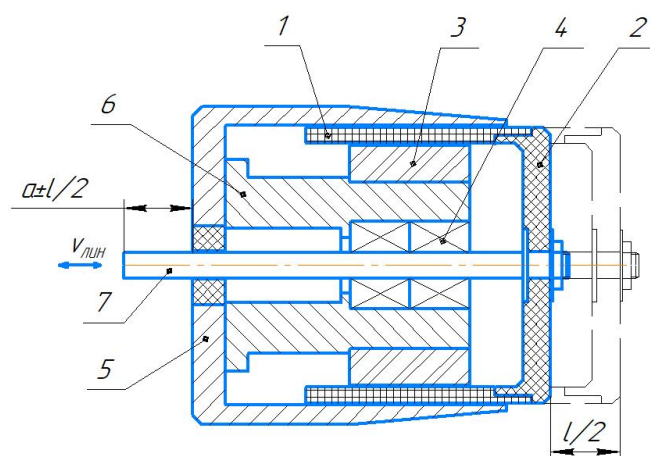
Линейный двигатель постоянного тока с полым якорем: 1 – катушка полового якоря; 2 – основание катушки; 3 – постоянный магнит; 4 – шарикоподшипники линейного типа; 5 – наружный магнитопровод; 6 – внутренний магнитопровод; 7 – рабочий шток
